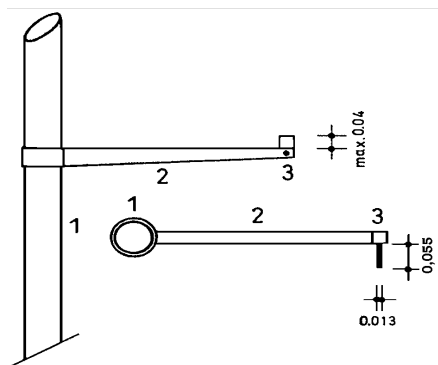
□ Soporte para el listón de pértiga, visto desde la colchoneta de caída y a vista de pájaro (Dimensiones en m.)
